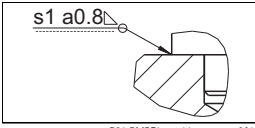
Variant U1: voorbereid voor aanbouw voorzetmembraan
